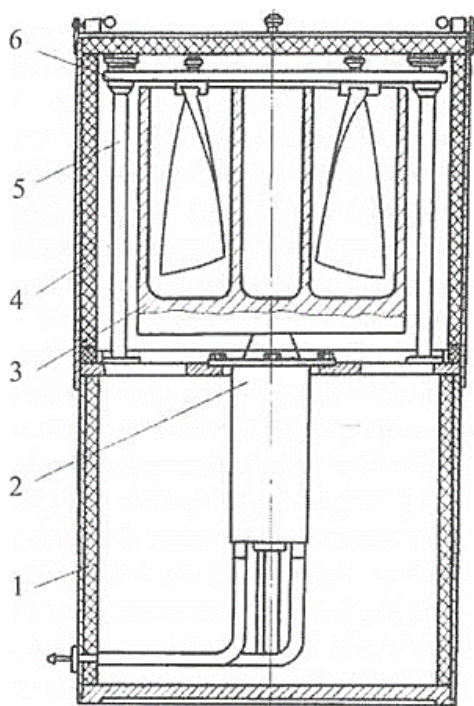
установка для ультразвукового деформаційного зміцнення лопаток: 1 – основа; 2 – ПМС15А-18; 3 – хвилевід; 4 – шумопоглинаючий кожух із кришкою; 5 – штанги; 6 – технологічний фланець.
